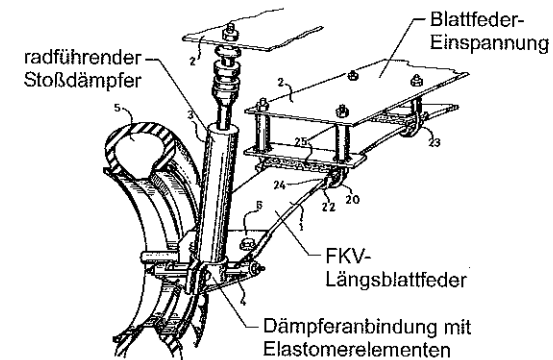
Als FKV-Kragträger ausgeführte Längsblattfeder-Radaufhängung von RENAULT [FPA83].
